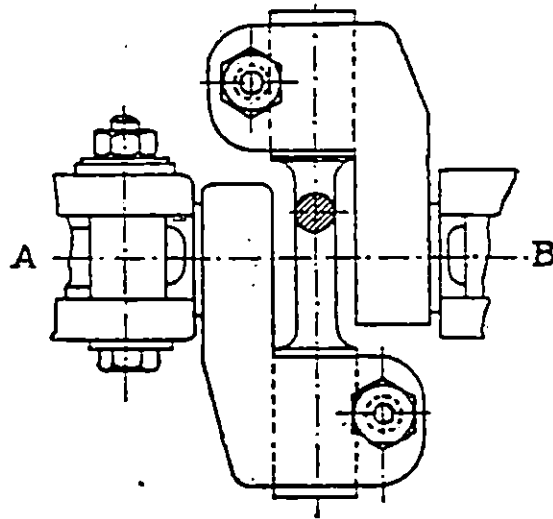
Dispositivo de ensayo de flexión plana Montano sobre Máquina de torsión Schenck.
